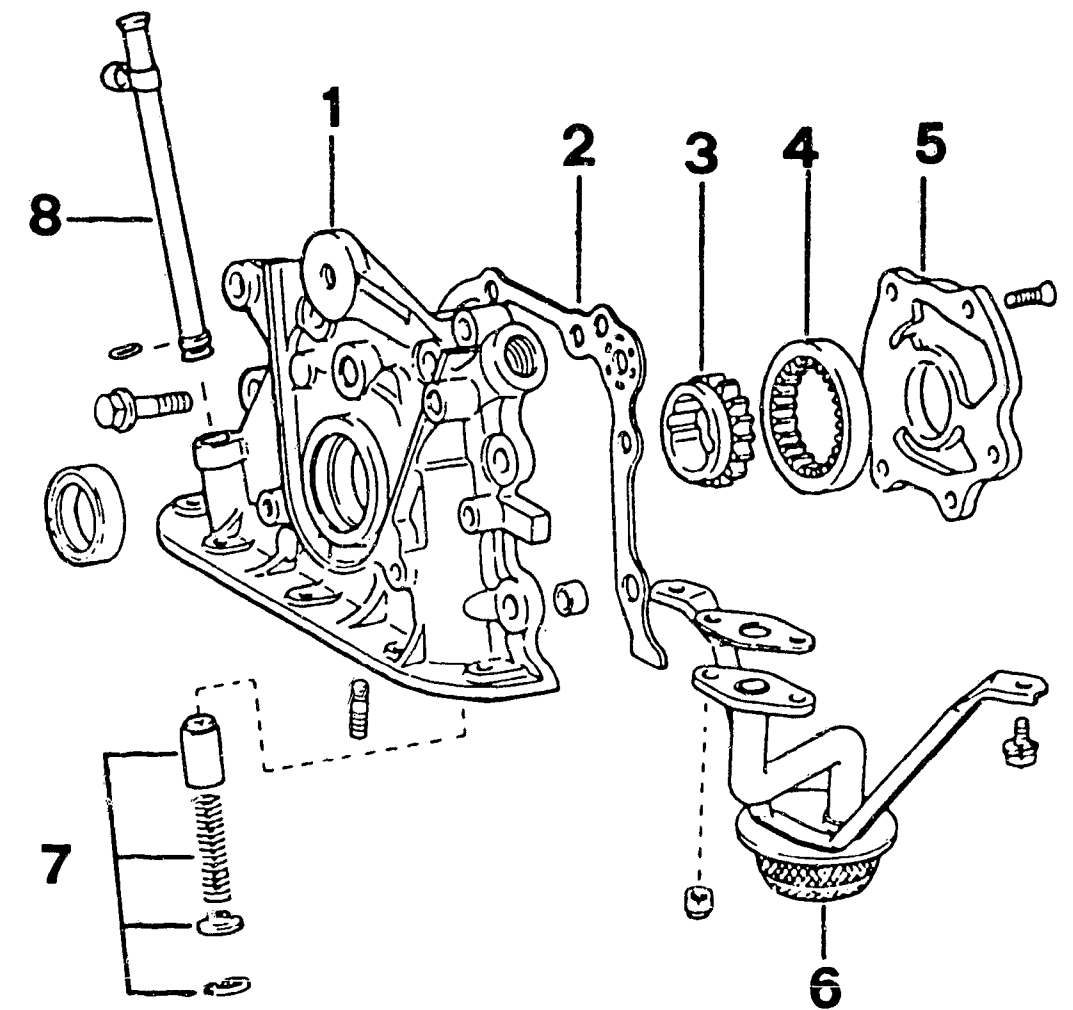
Motoren 4A-C und 4A-GE: Einzelteile der Ölpumpe. 1 Stirnraddeckel – 2 Dichtung – 3 Innenrad – 4 Aussenrad – 5 Ölpumpengehäuse – 6 Ölsaugsieb – 7 Überdruckventil – 8 Ölmesstabführung.
